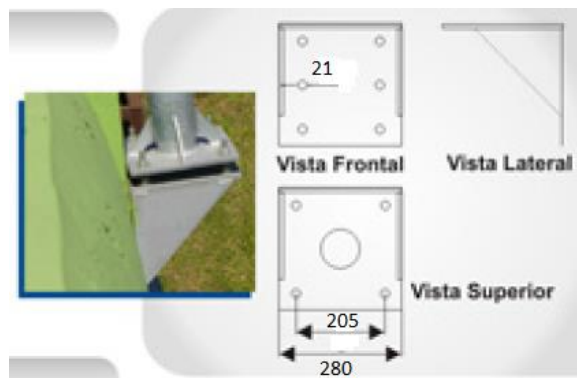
FIXAÇÃO LATERAL EM MURETA
